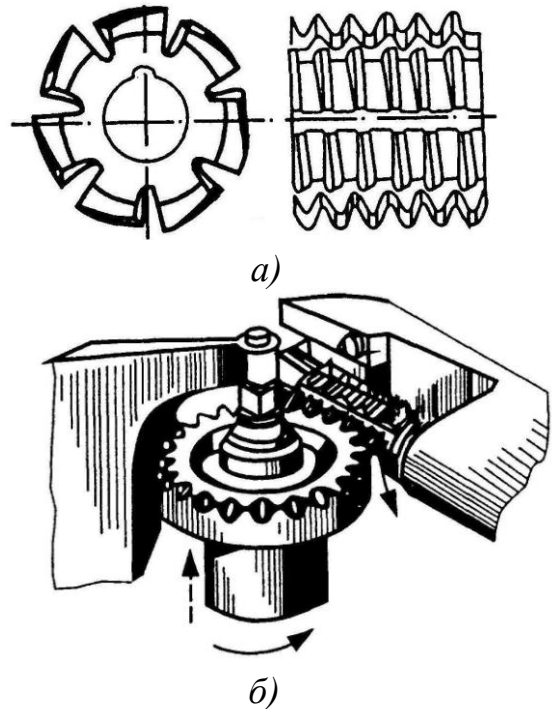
Нарізання зубчатих коліс черв'ячною фрезою
